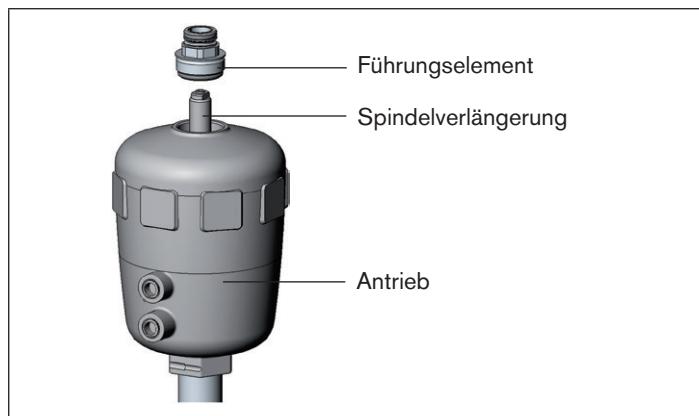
Montage der Schaltspindel, Reihe 26xx und 27xx - 1
